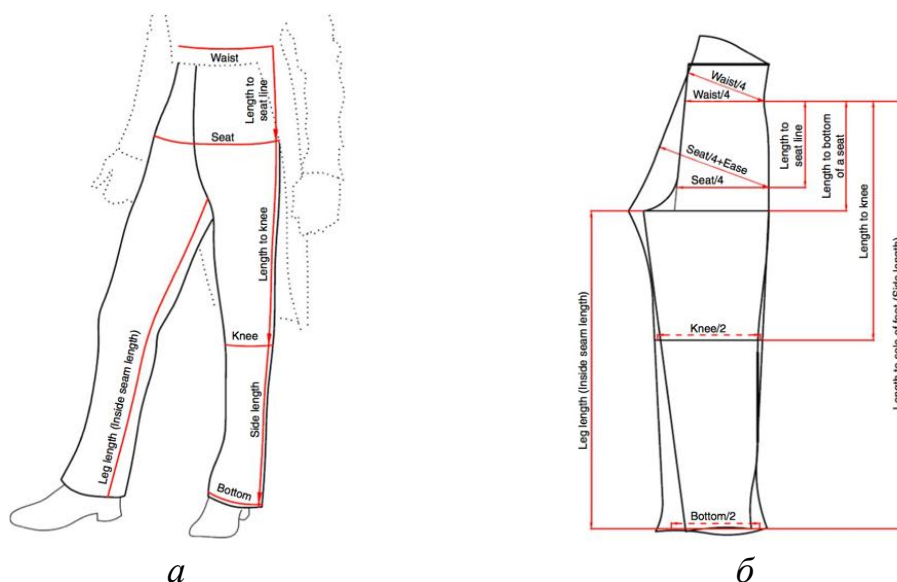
Размерные признаки для составления чертежа брюк:
